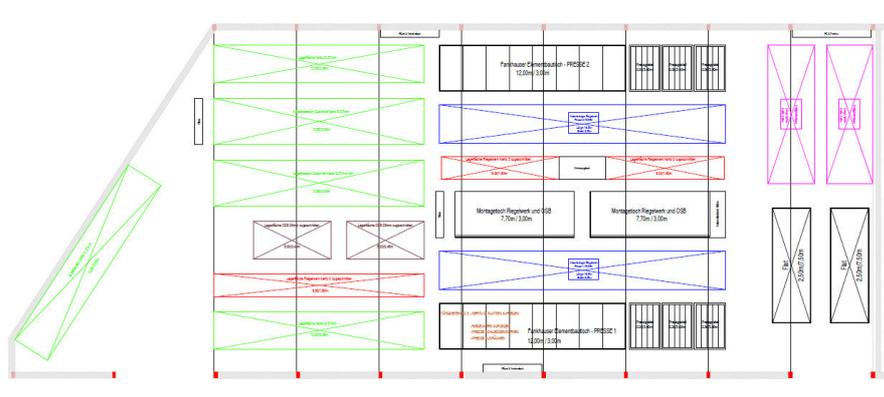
Endgültiger Halleneinrichtungsplan (Projekt B)⁴³²
